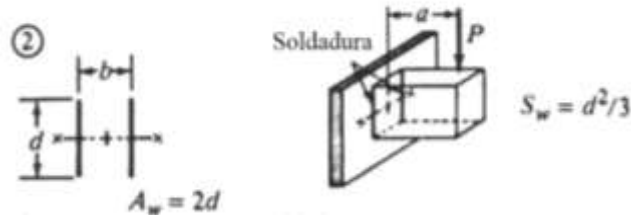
Factor geométrico para analizar la soldadura como una línea.
